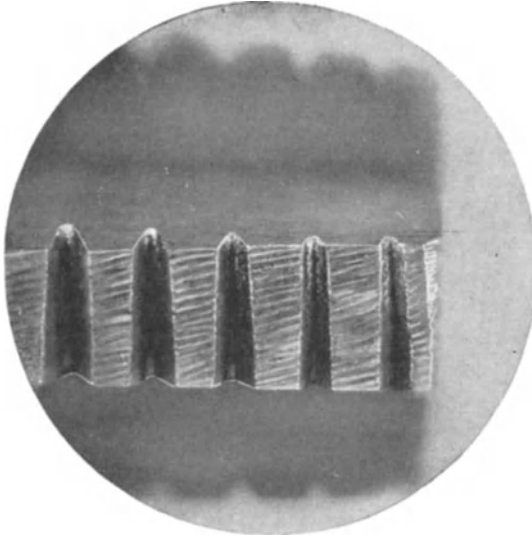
Im Anschnitt hinterfeilter Gewindebohrer.
